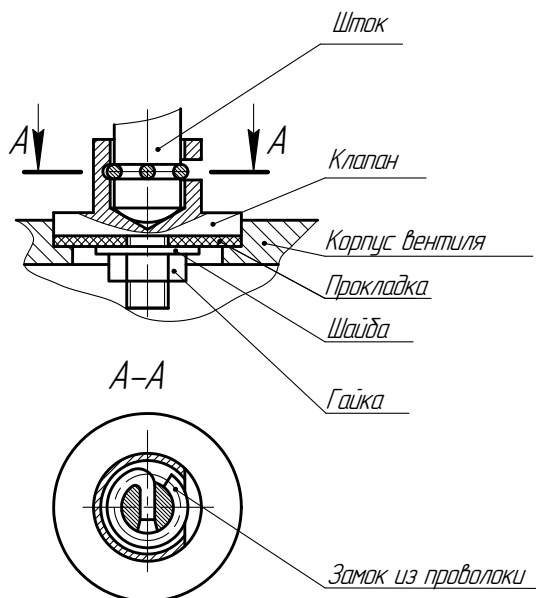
Крепление штока к клапану при помощи проволочного замка
